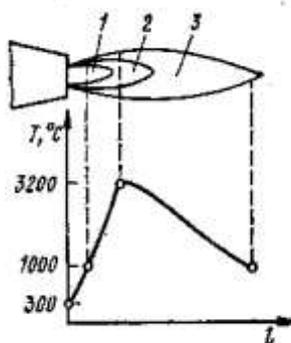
Газосварочное пламя, образованное газосварочной горелкой
